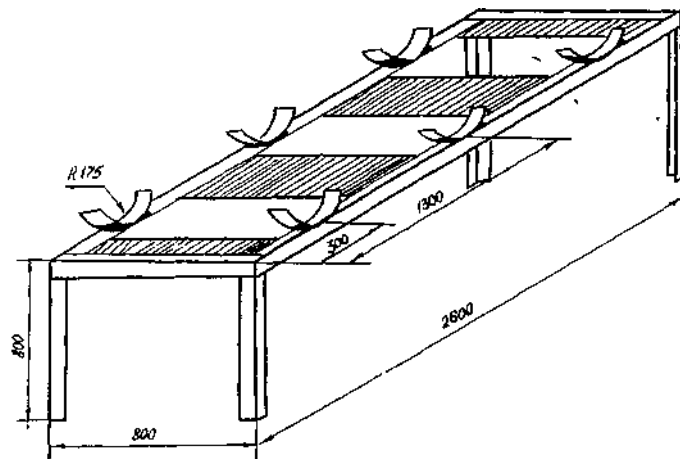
Верстак для разборки и сборки дугогасительных камер.
